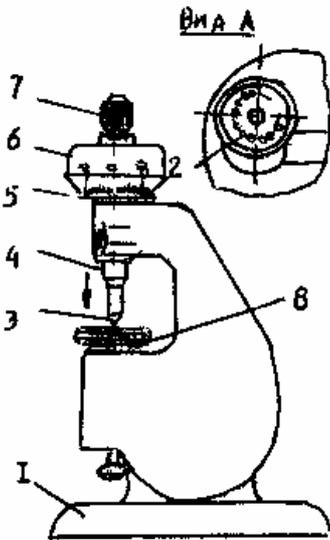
Микрометр настольный вертикальный: 1 – корпус, 2 – поворотный лист, 3 – измерительный наконечник, 4 – подвижный измерительный стержень, 5 – стержень, 6 – барабан, 7 – фрикцион, 8 – измерительный стол
